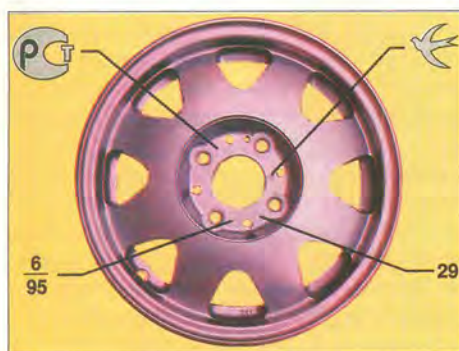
Маркировка на колесе (сверху по часовой стрелке): клеймо, свидетельствующее о сертификации в Госстандарте России; товарный знак завода-изготовителя (БКМПО); вылет (29 мм); месяц и год изготовления (июнь, 1995 г.).
